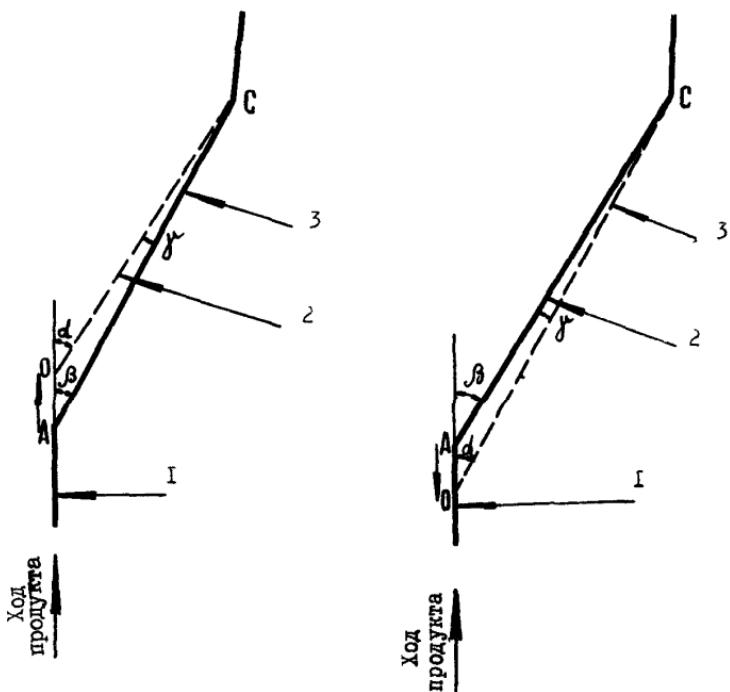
Перемещение вершины индивидуального угла вперед (первый способ):
